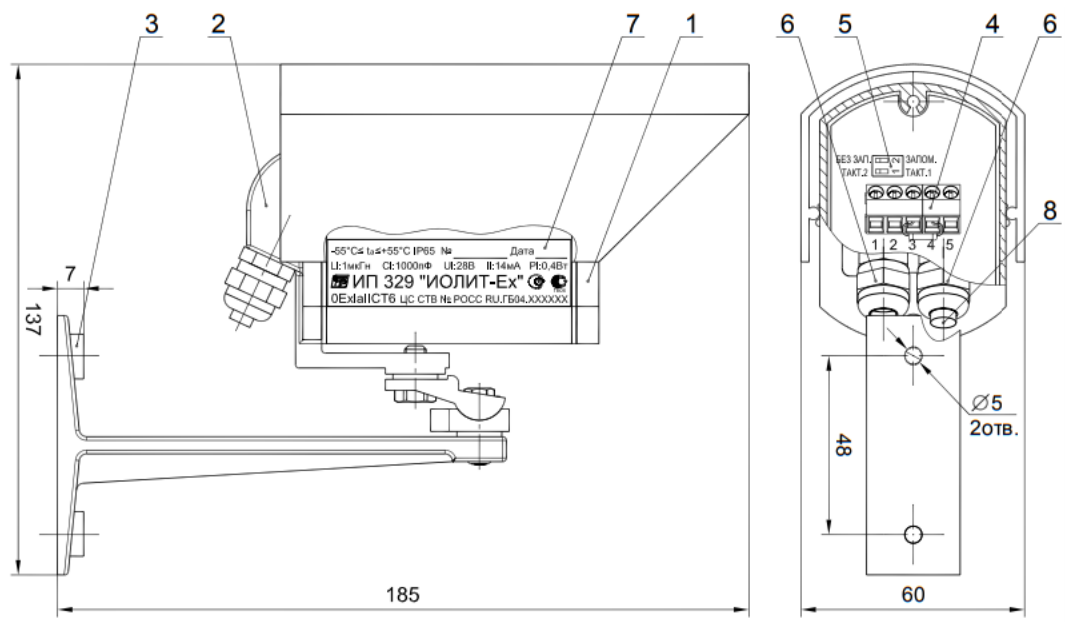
Общий вид извещателя ИП 329 «ИОЛИТ»
